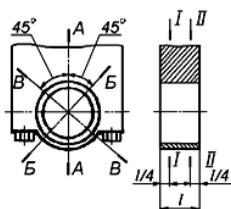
Схема замеров отверстия опор коренных подшипников блока:
